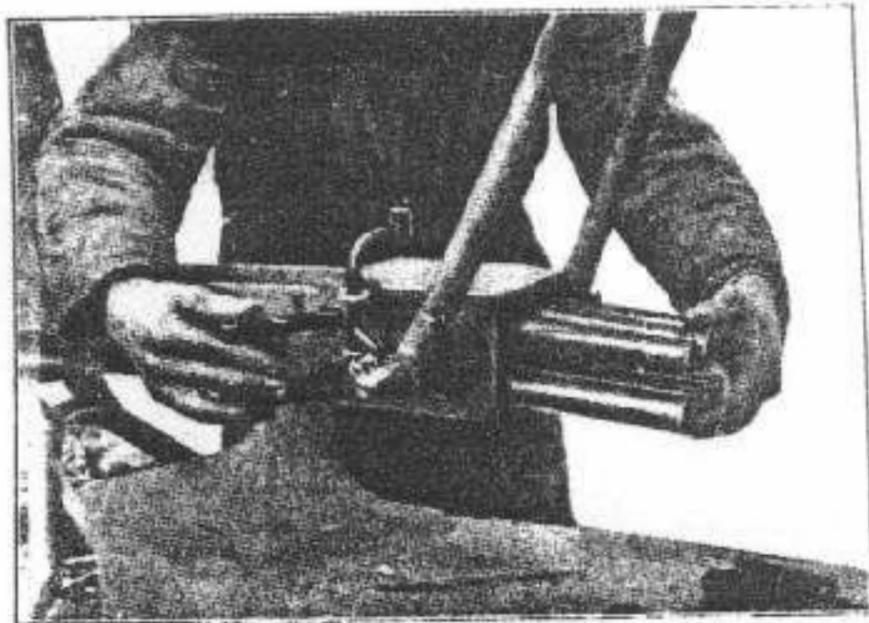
Come si levano le due cremagliere e il gruppo tubi reggi molla.
